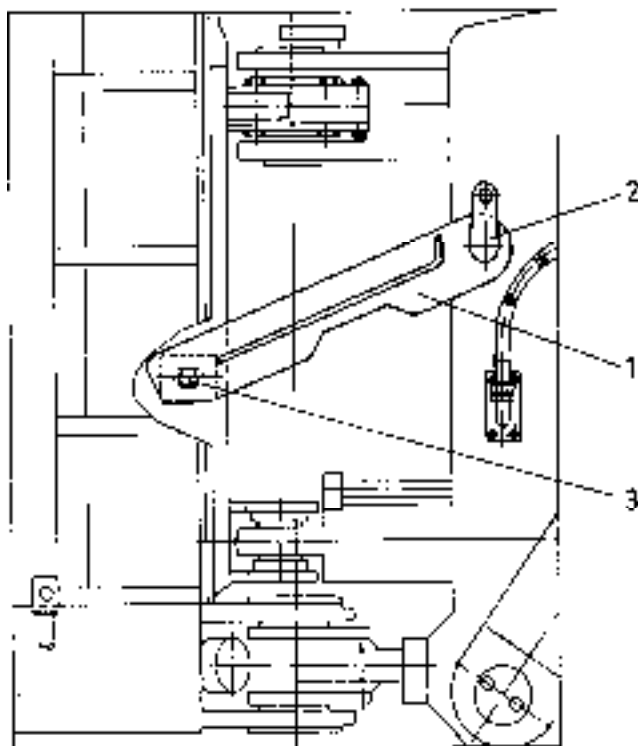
Соединитель и шкворни в положении блокировки рам
